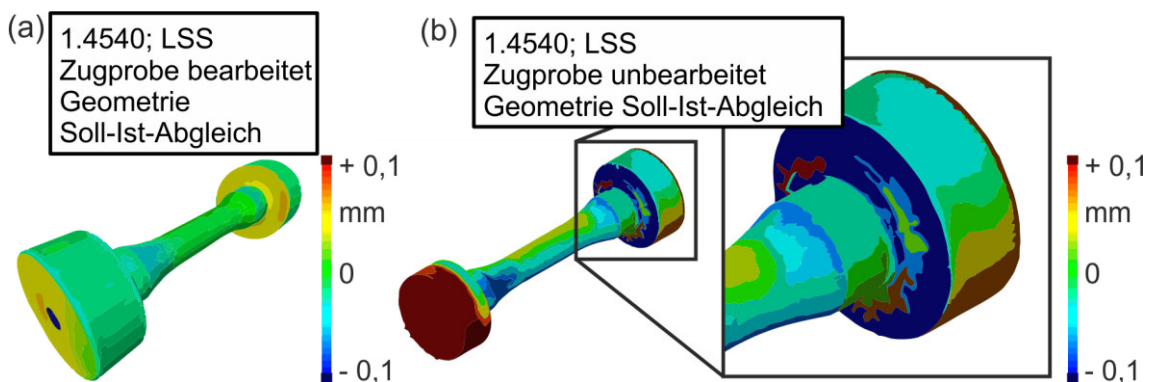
Soll-Ist-Abgleich der Geometrie einer exemplarischen (a) bearbeiteten und (b) unbearbeiteten laserstrahlgeschmolzenen Zugproben
